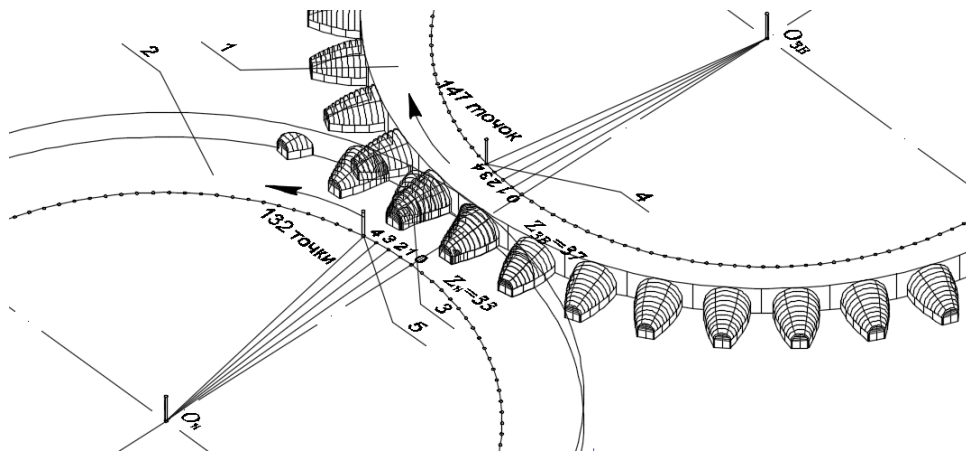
Модель створення зубчастого зачеплення зубозаокруглюючих впадин накатника та фрагменту зубчастого вінця шестерні коробки передач автомобіля: 1 – 3d-модель зубчастого вінця; 2 – 3d-модель обробленої заготовки; 3 – 3d-модель утвореної зубозаокруглюючої впадини; 4, 5 – орієнтувальні мітки зубчастого вінця та заготовки відповідно
